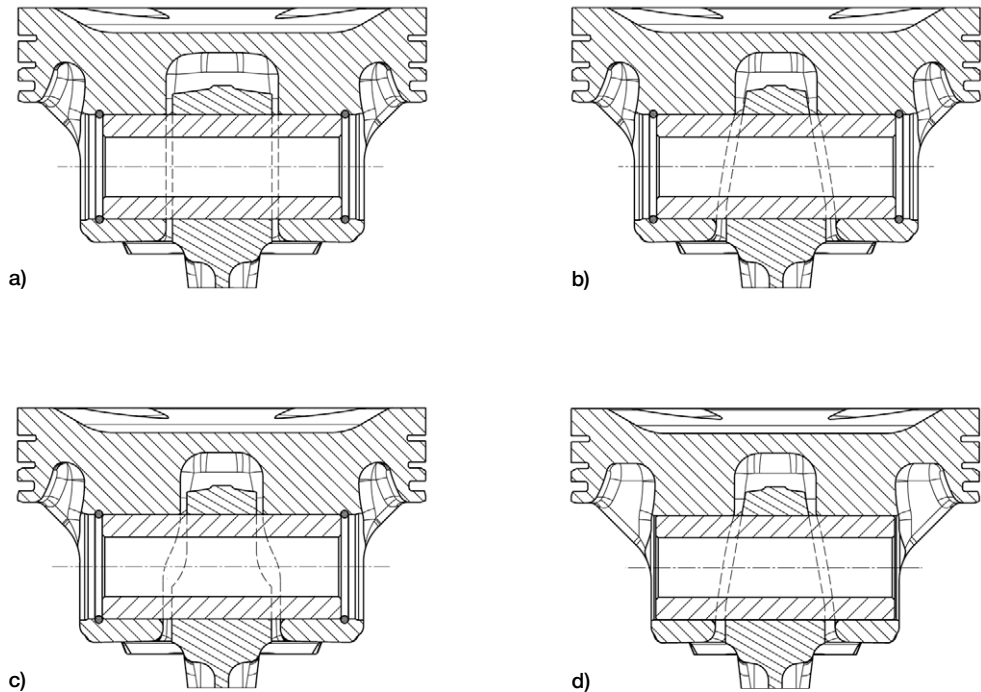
a) Schwimmende Lagerung mit Parallelabstützung, b) Schwimmende Lagerung mit Trapezabstützung, c) Schwimmende Lagerung mit Stufenabstützung, d) Klemmpleuel
